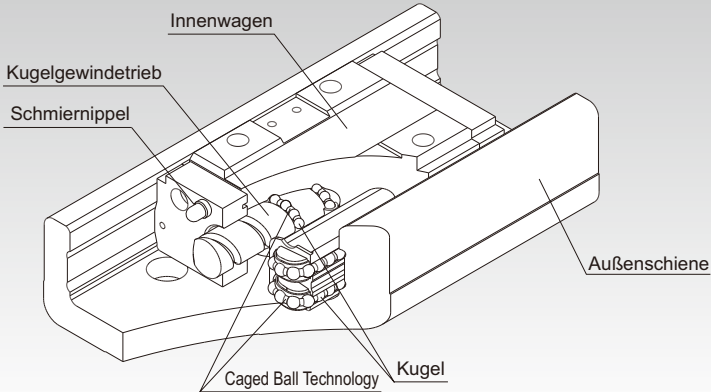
Aufbau der Linearachse SKR mit Caged Technology
